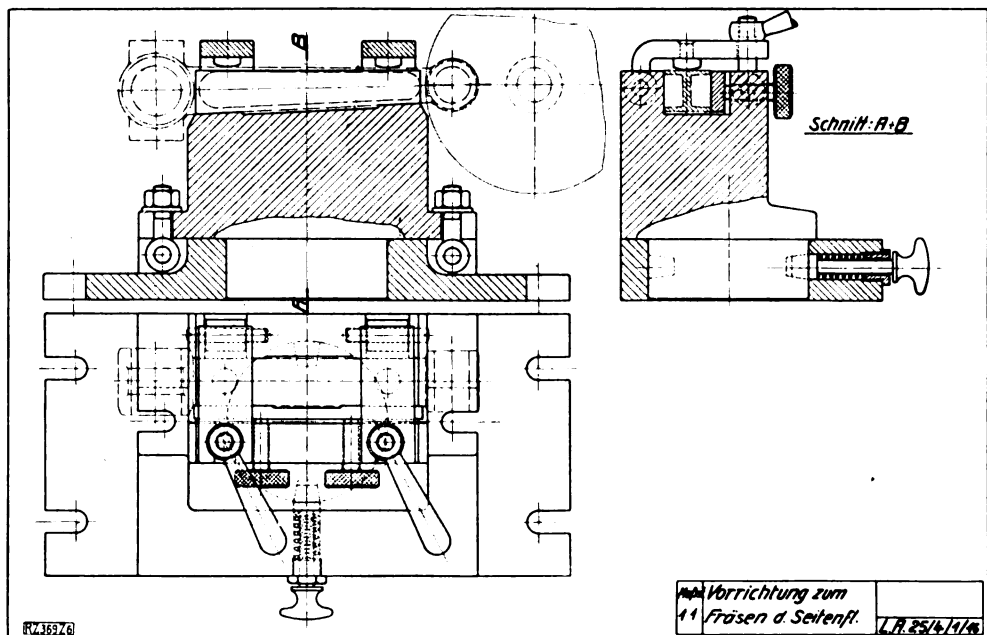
Fräsvorrichtung für Schubstange, angefertigt in den Zeichenübungen für Werkzeugmaschinen an der Maschinenbauschule Köln.
